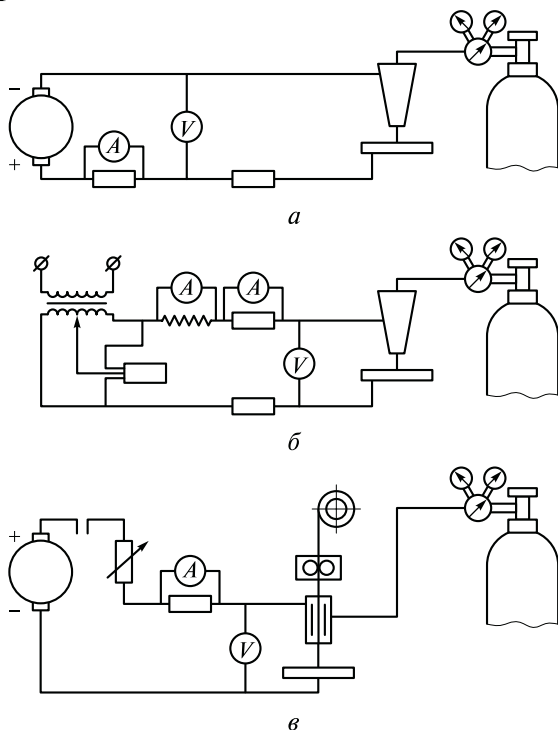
Схемы постов для сварки в защитных газах:
